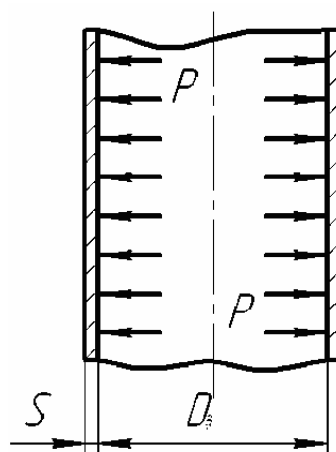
Розрахункова схема циліндричної обичайки пропанової колони
